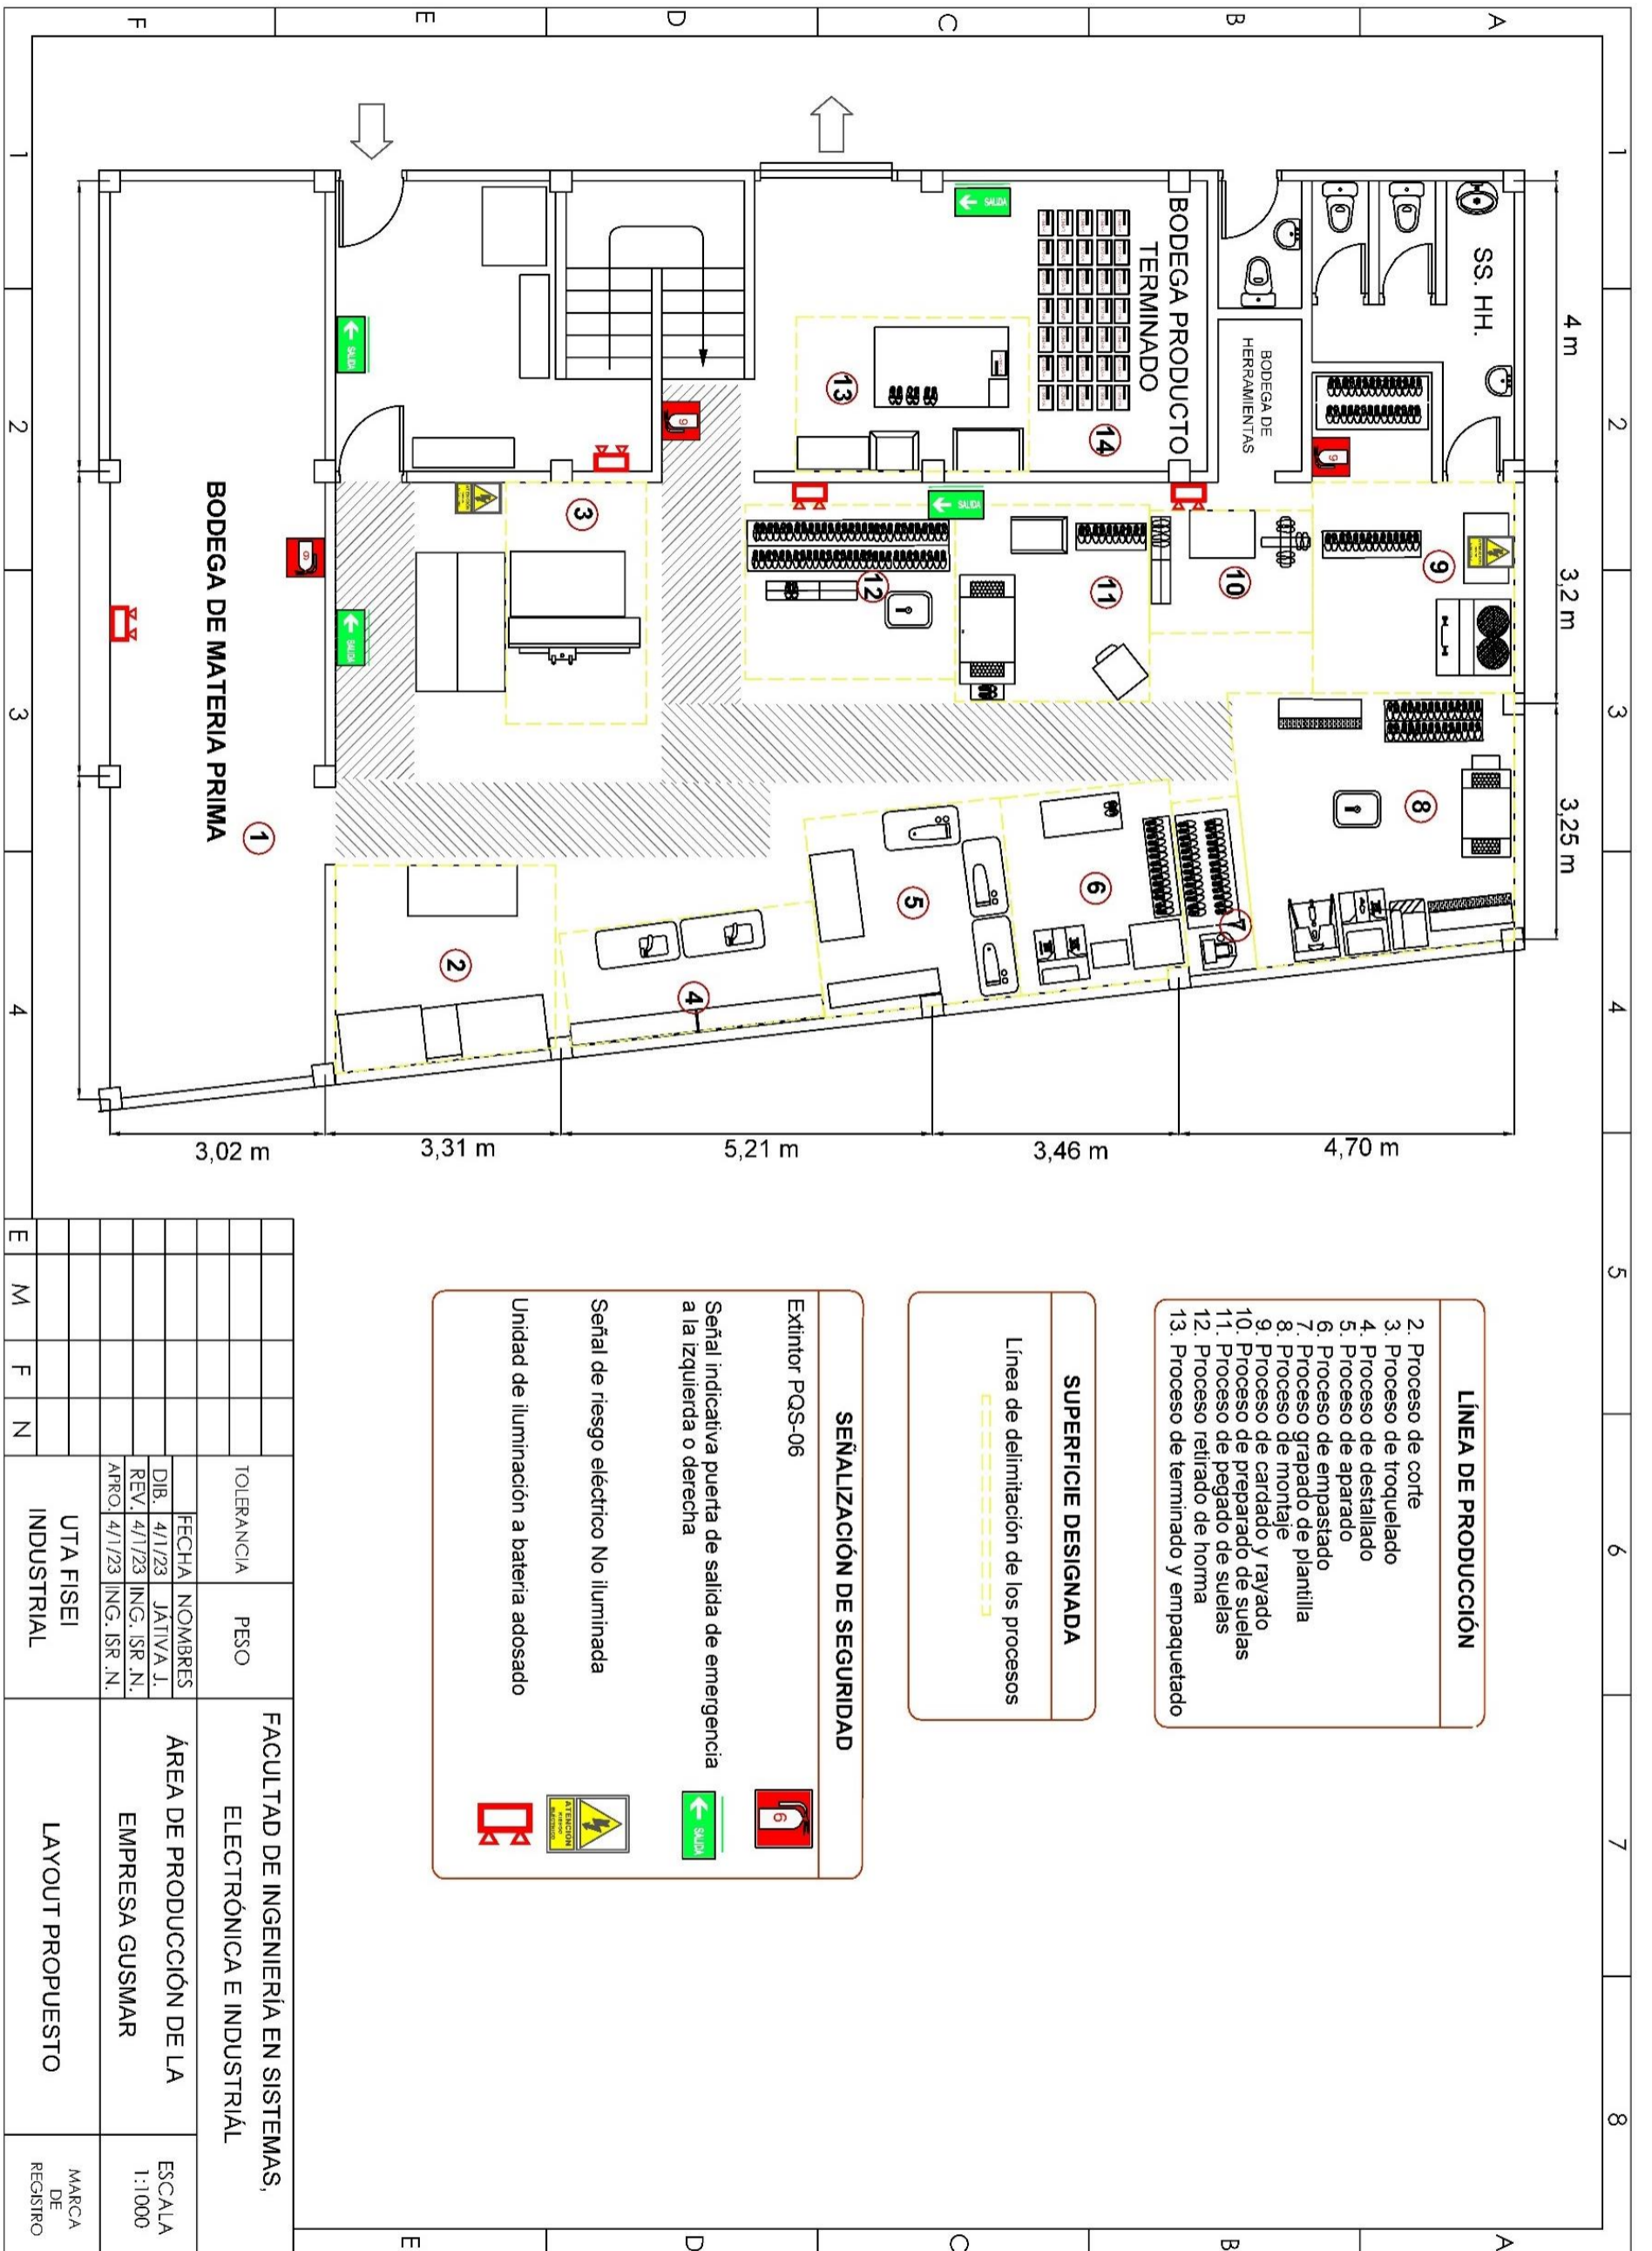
Layout propuesto de redistribución de planta en la empresa GUSMAR.
